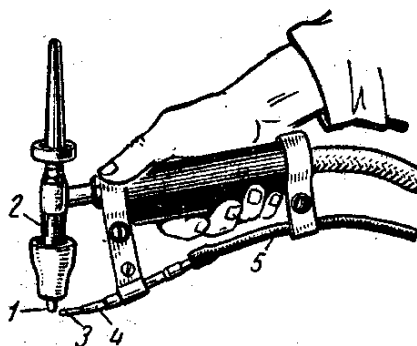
Горелка - держатель к полуавтомату для сварки вольфрамовым электродом с присадочной проволокой
